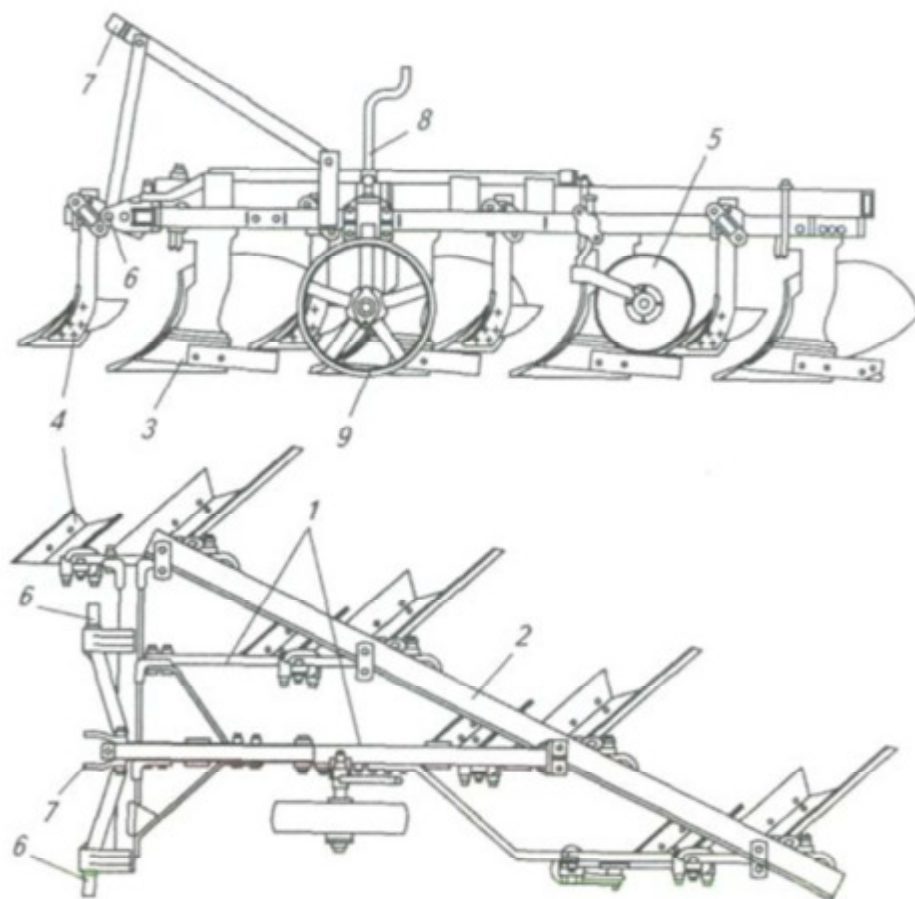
Навесной четырехкорпусный плуг общего назначения
